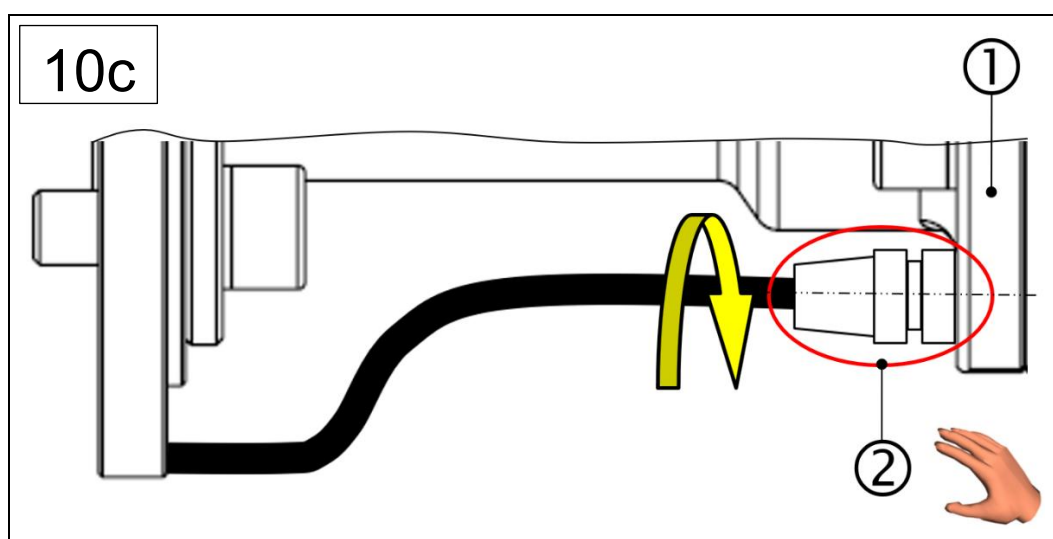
Montaggio dell'unità sensore, BEAROMOS® 2020 (variante corta, passaggi 1-10)
